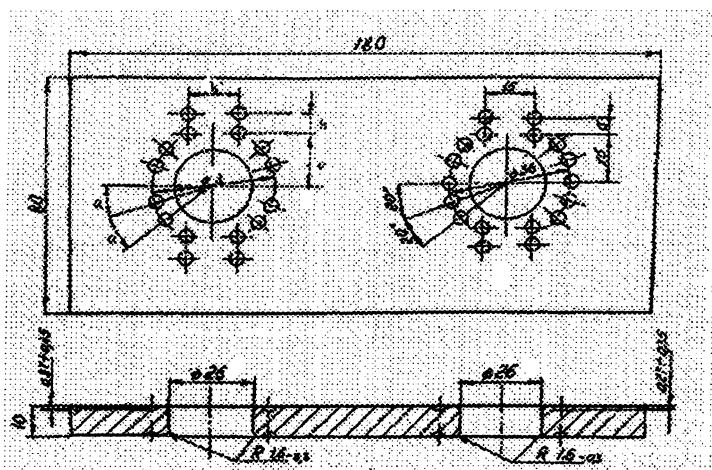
Плоский образец для усталостных испытаний в условиях фреттинга
